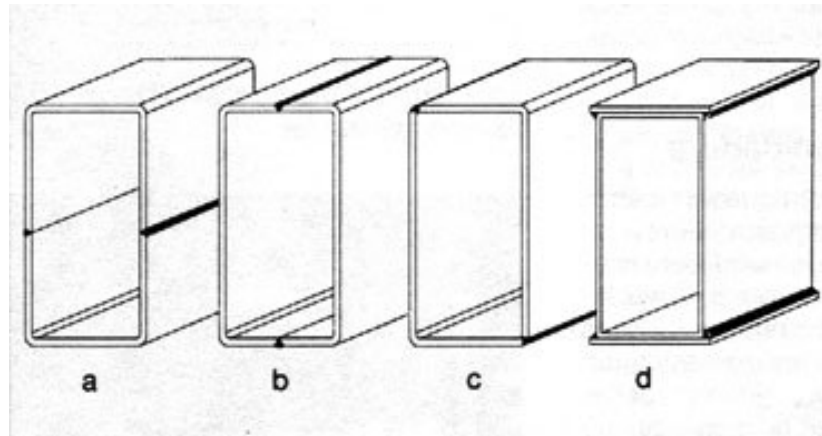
Diseño de vigas cajón soldadas. Diseños (a) y (b) aceptables. Diseños (c) y (d) no recomendables
